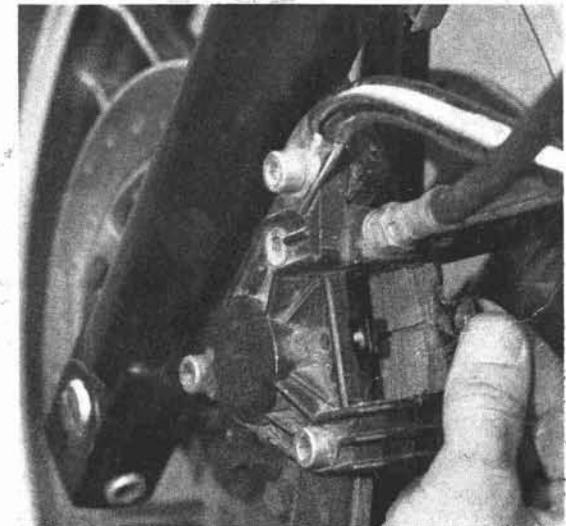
Dépose des plaquettes (Photo RMT)
